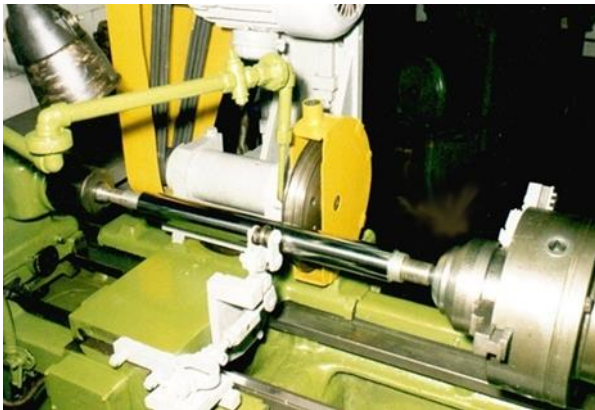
Установка для механоімпульсної обробки циліндричних поверхонь
